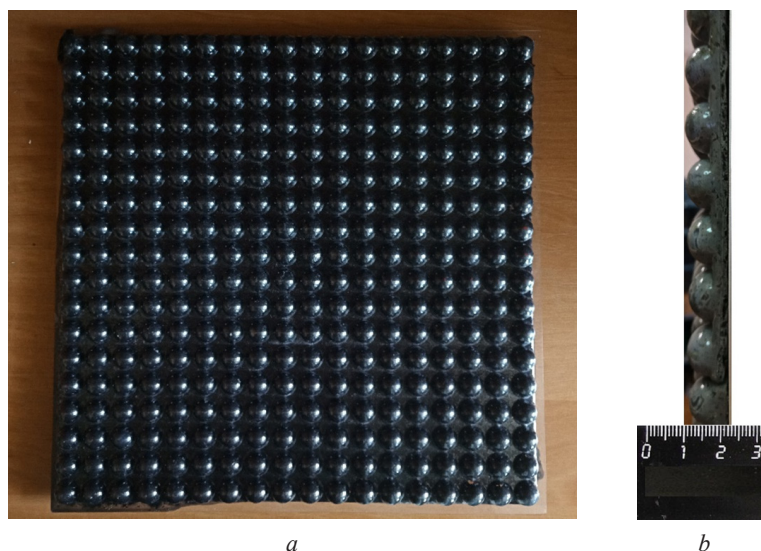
Внешний вид сверху одного из изготовленных экспериментальных образцов (*a*) и внешний вид сбоку фрагмента одного из полученных образцов (*b*)
